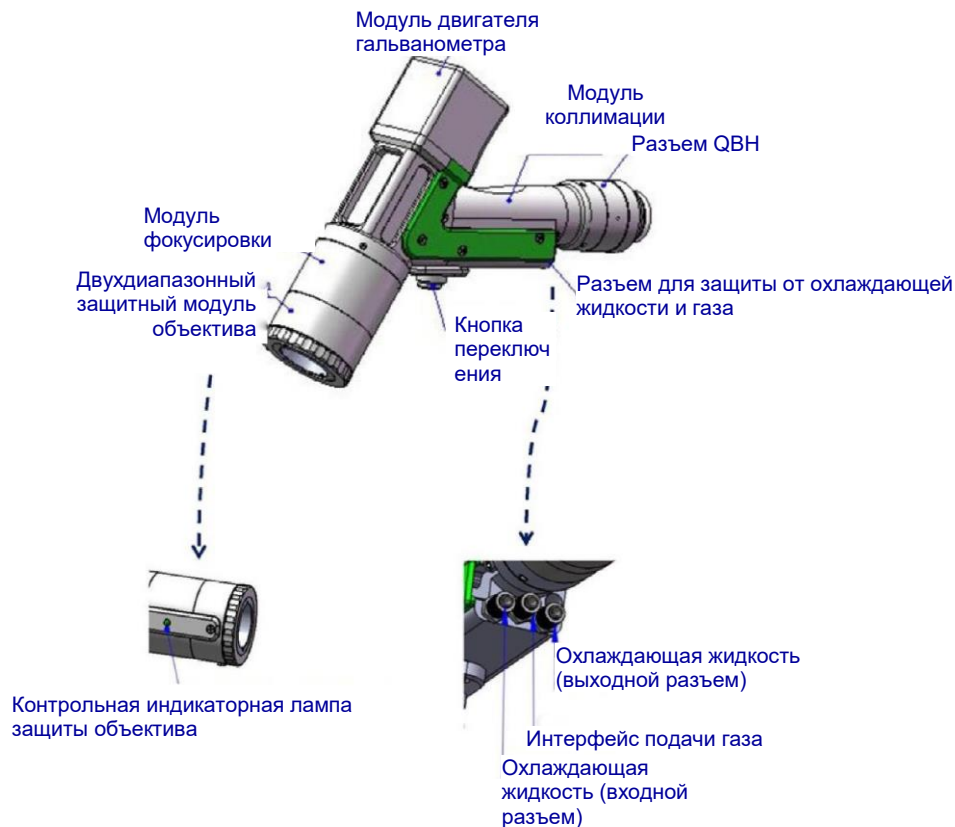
Структурная схема ручного излучателя установки для очистки
